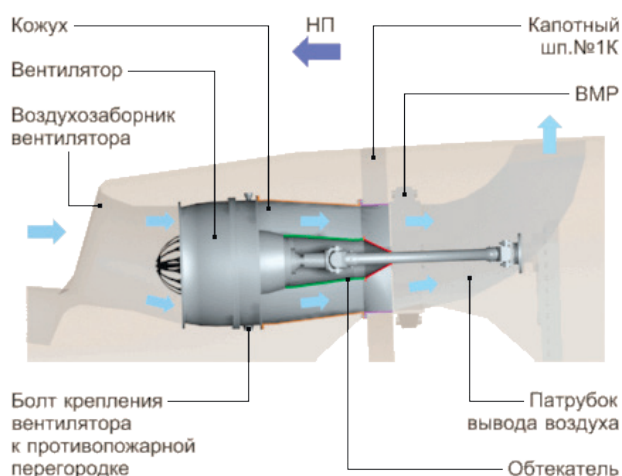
Вентиляторная установка вертолета Ми-8.
